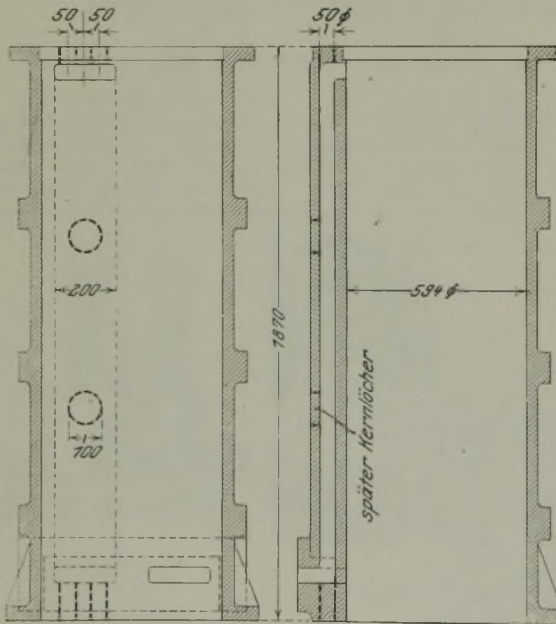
Dampfzylinder für einen 3000-kg-Hammer.
